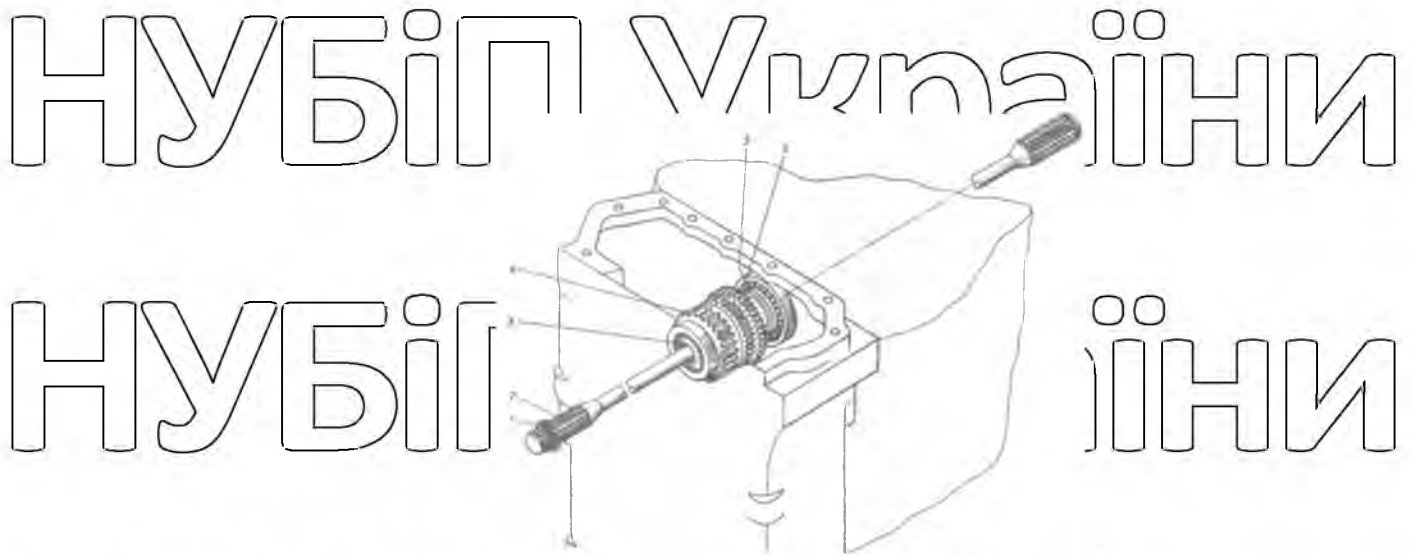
Зняття валу і коліс зубчастих приводу ВОМ :
